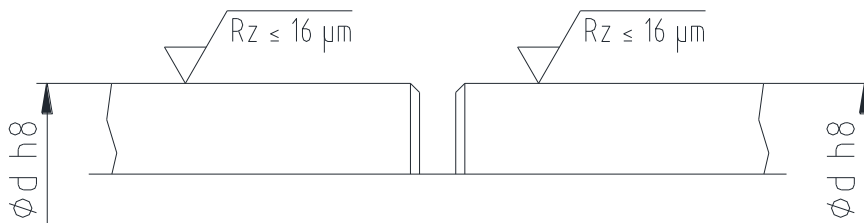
Toleranzen und Oberflächen (Beispiel: CLAMPEX® KTR 700)
